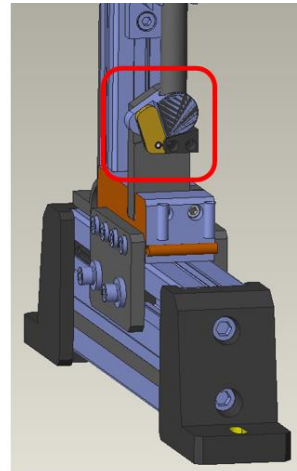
Colocador de soldadura após o sistema de fixação ser alterado
